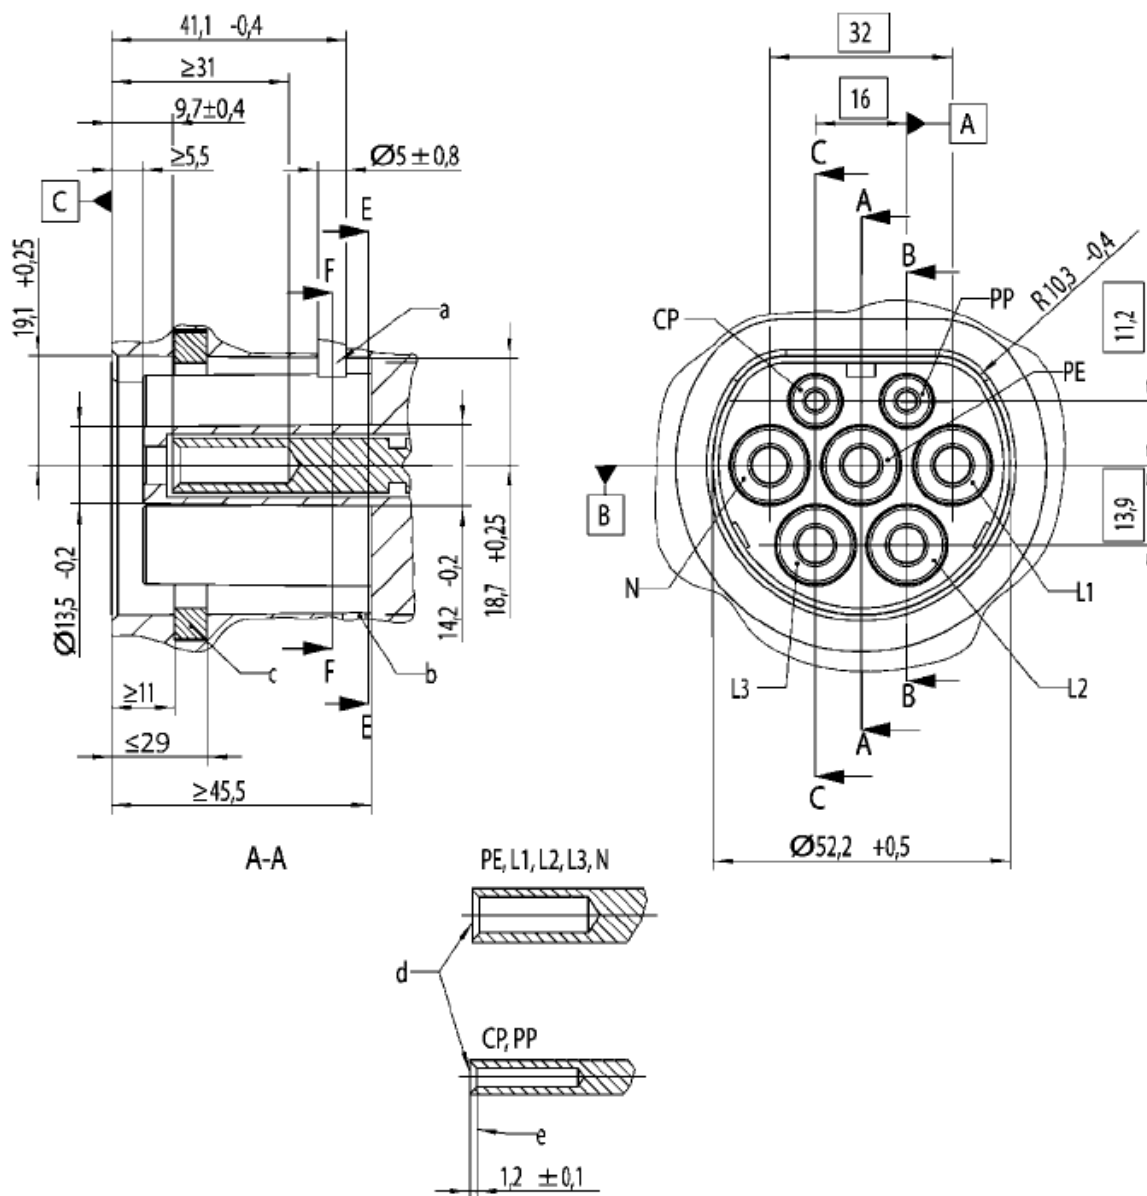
Dimensjonsblad for DC-kontakten i henhold til IEC 62196-3:2022
